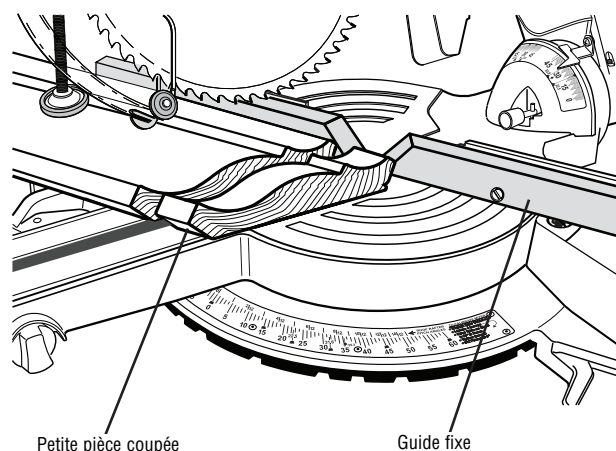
Pièce coupée arrêtée par le guide auxiliaire
